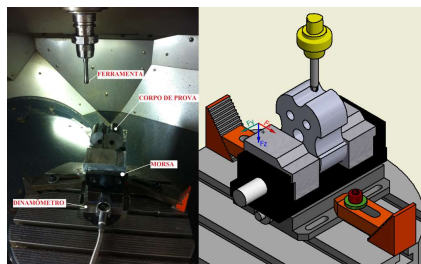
Corpo de prova montado na máquina sobre o dinamômetro.
